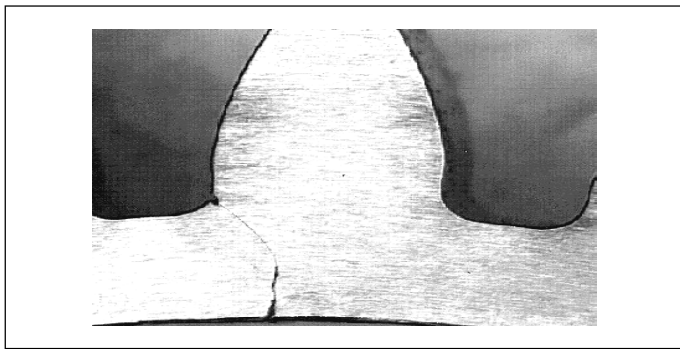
Grieta de fractura por la llanta de una rueda dentada [7]
